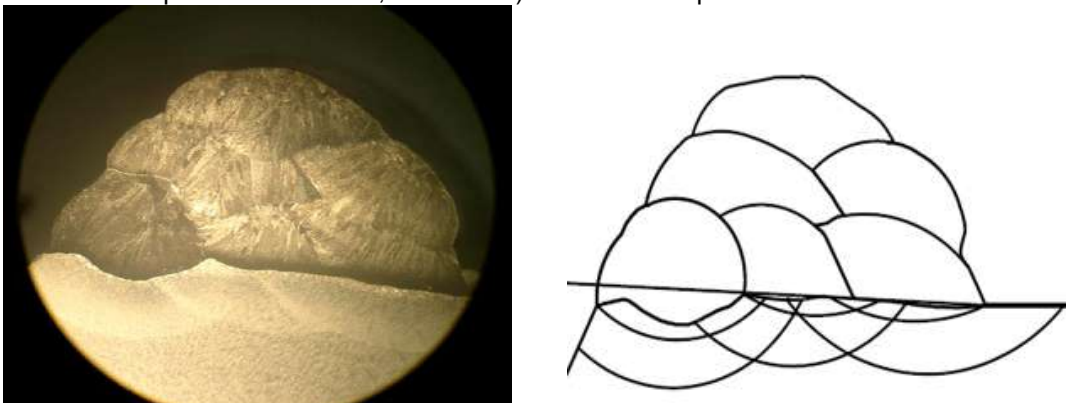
a) Macrografia da amostra pré-teste do amantecimento, soldagem tripla camada por processo GMAW com aporte térmico de 0,9 kJ/mm. b) Desenho computacional da amostra pré-teste amantecimento.
